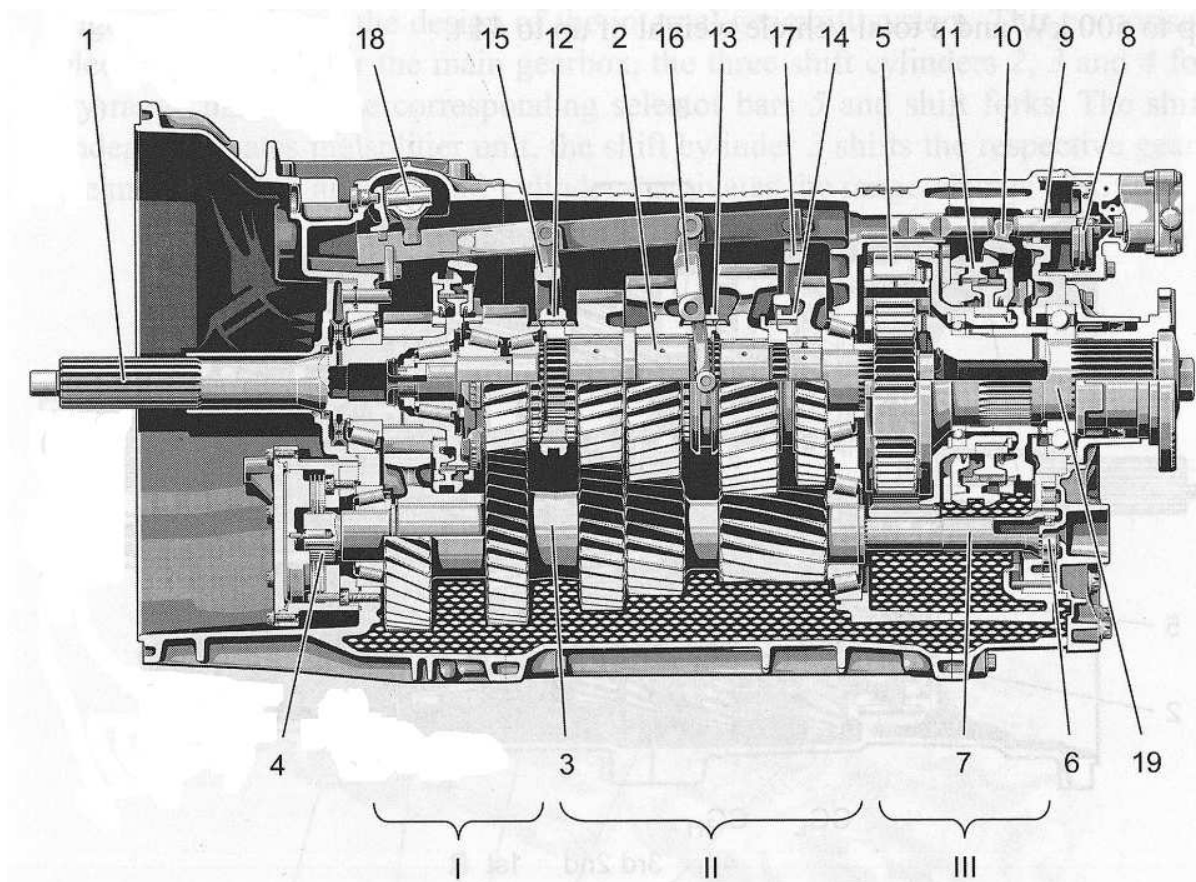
Transmissão "Full Power Shift". I grupo desmultiplicador; II transmissão principal; III grupo redutor; 1 eixo de entrada; 2 eixo principal; 3 eixo intermediário; 4 freio do eixo intermediário; 5 engrenagem planetária; 6 bomba de óleo; 7 eixo da bomba de óleo; 8 cilindro atuador pneumático; 9 haste do cilindro; 10 garfo; 11 luva deslizante; 12/13/14 luvas deslizantes da transmissão principal; 15/16/17 garfos da transmissão principal; 18 eixo seletor; 19 eixo de saída.
